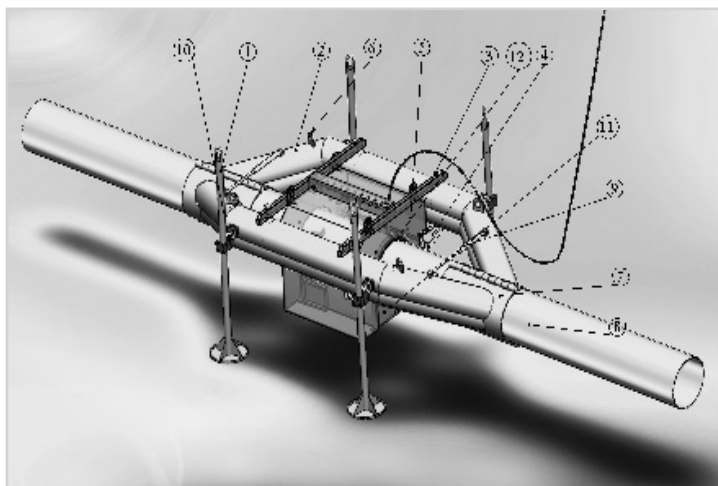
Общий вид подводного сварочного комплекса: опора – 1; установочная рама – 2; опорная балка – 3; откидной упор – 4; корпус кессона – 5; грузовая проушина – 6; трубный захват – 7; трубопровод – 8; гидронатяжитель – 9; герметизирующие створки – 10; камера для сухой сварки – 11; пневматическое уплотнение – 12.
